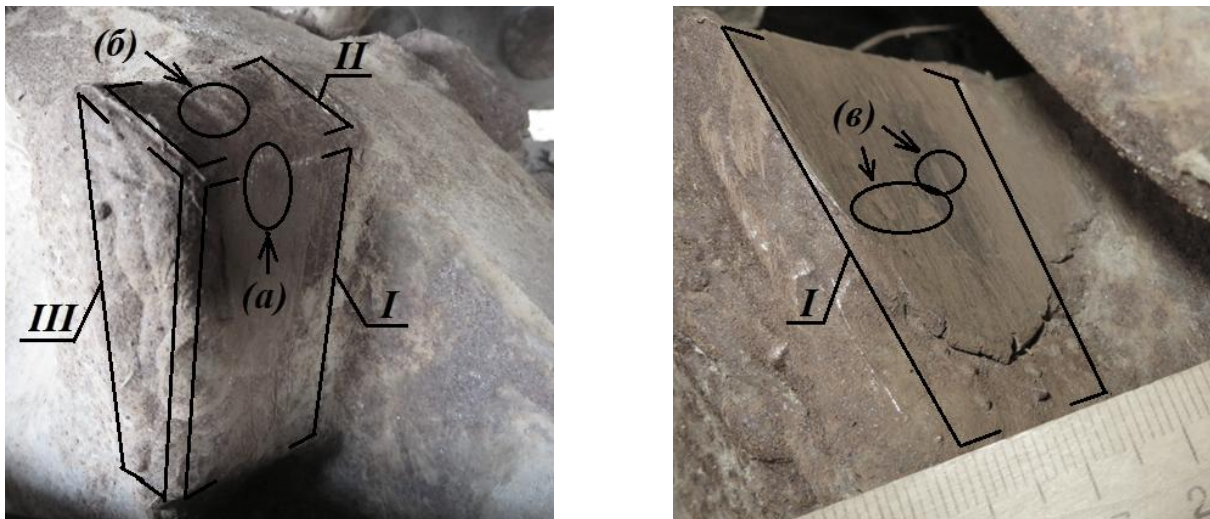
Характер изнашивания рабочих поверхностей зубьев (1) и (2) ведущего колеса: I – III – условные поверхности зуба; (а–в) – повреждения поверхностей зуба
